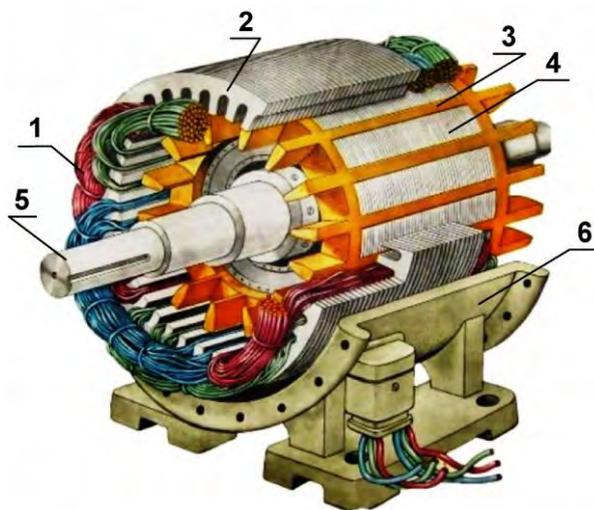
Асинхронный двигатель: 1 – обмотка статора; 2 – сердечник статора; 3 – «беличья клетка»; 4 – сердечник ротора; 5 – вал ротора; 6 – станина
